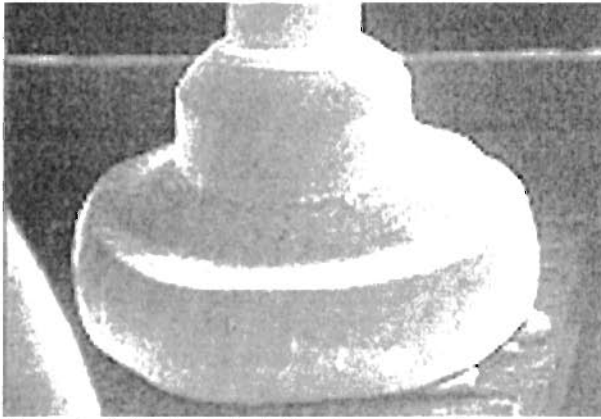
Soldado de bola (hecho con una herramienta de soldado APROVA).
